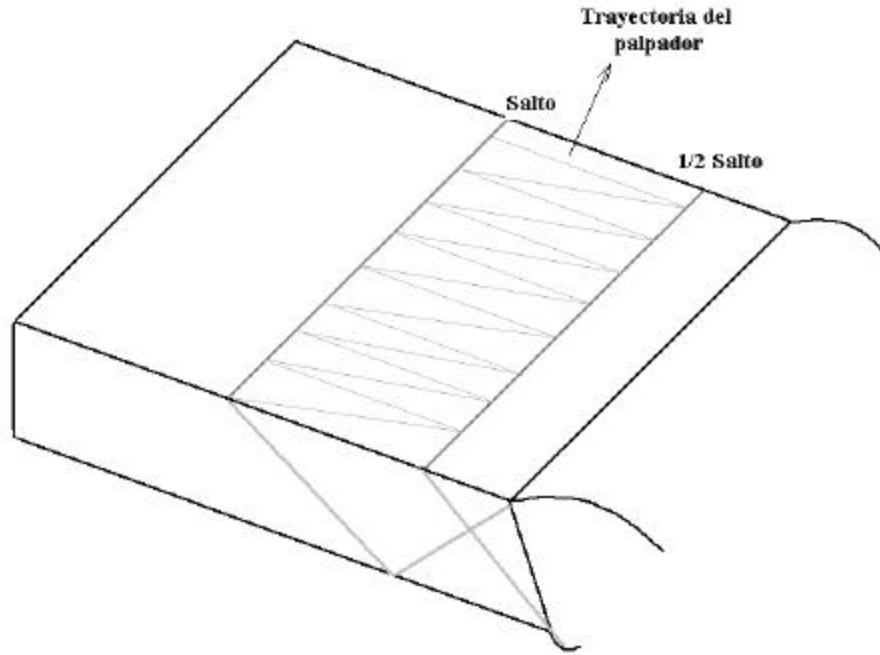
Inspección del cordón de soldadura.
